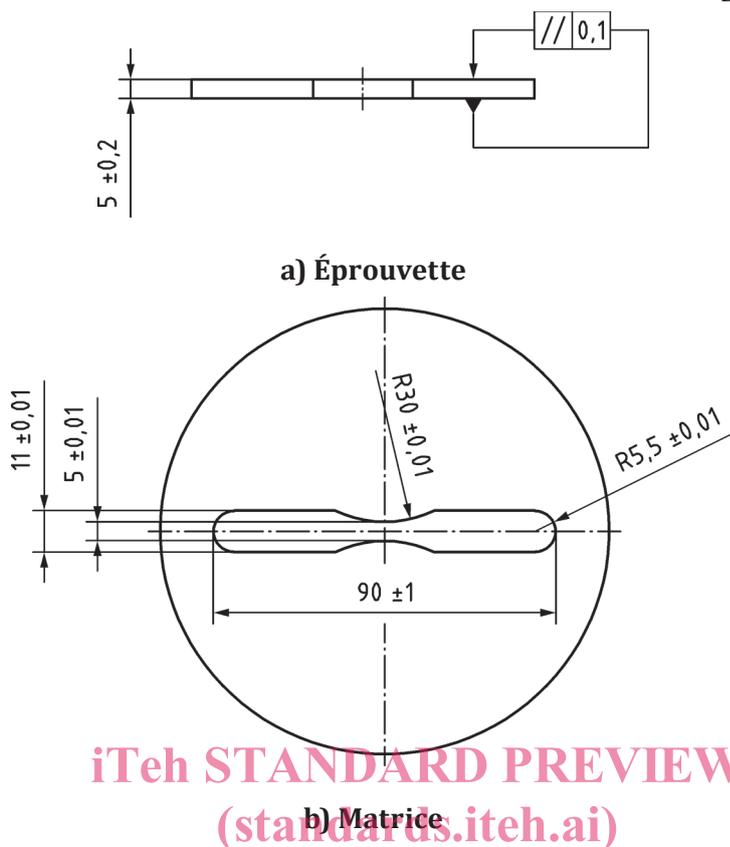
Éprouvette sans entaille et matrice de compression utilisée pour former des éprouvettes sans entaille destinées à des essais de fatigue
